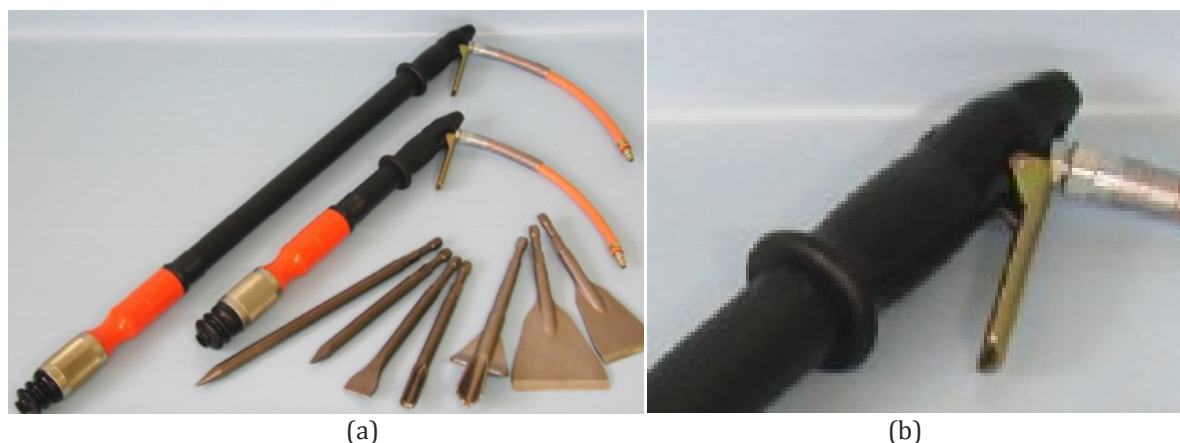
Marteau burineur pneumatique Scrap'air (a) et le sous-ensemble « vanne » (b)
